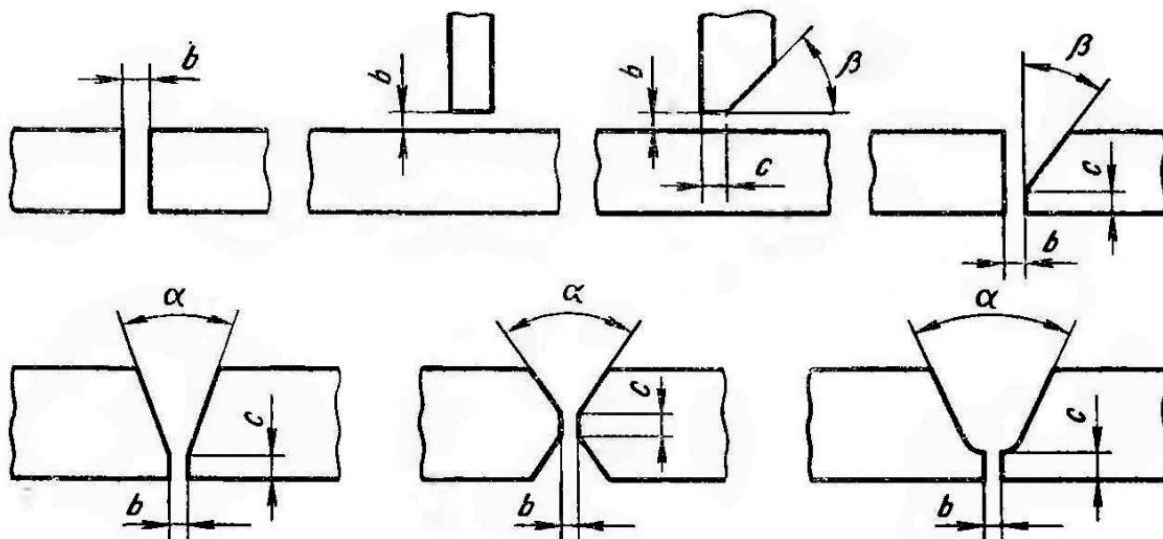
формы подготовки кромок под сварку при ручной дуговой и автоматической сварке под флюсом
